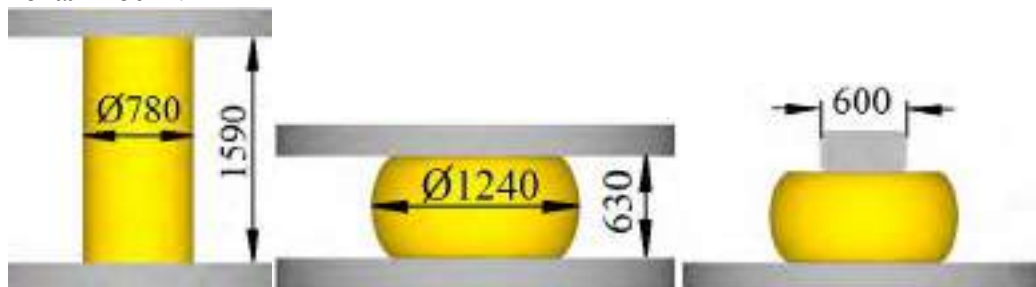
Схема процесса осадки заготовки плоскими плитами
